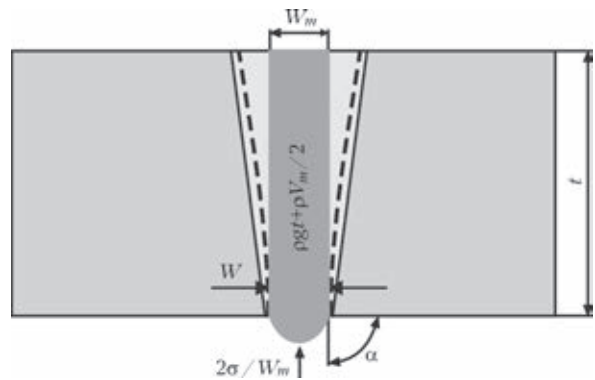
Баланс давлений в корневой части сварочной ванны [6]
